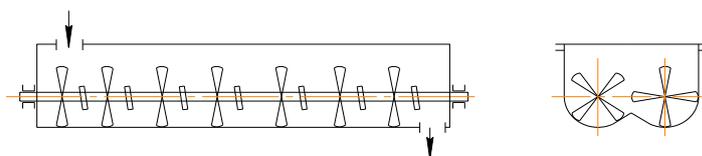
Горизонтальный двухвальный смеситель непрерывного действия
